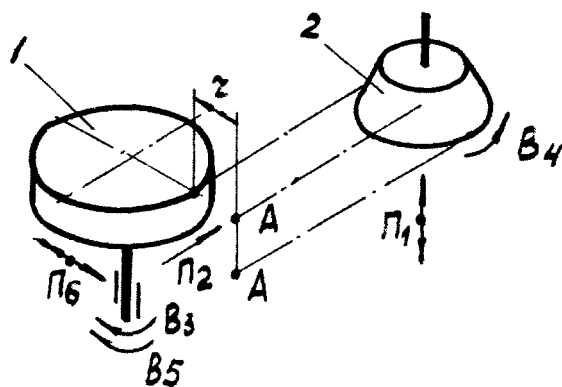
Способ долбления цилиндрических зубчатых колес при касательном движении врезания
